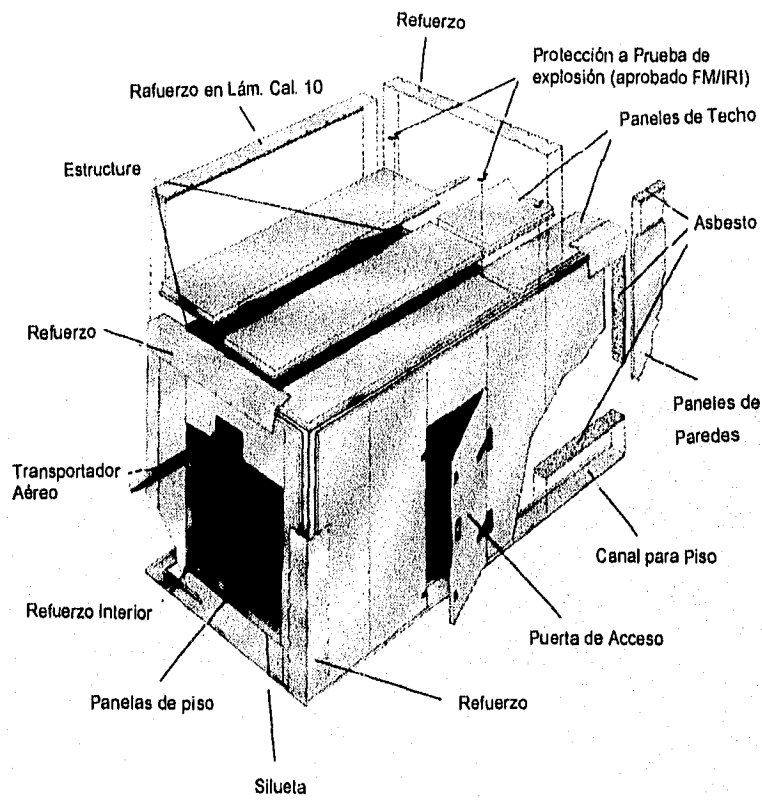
4 Explosión de un ensamble de horno con paneles telescopiados.
